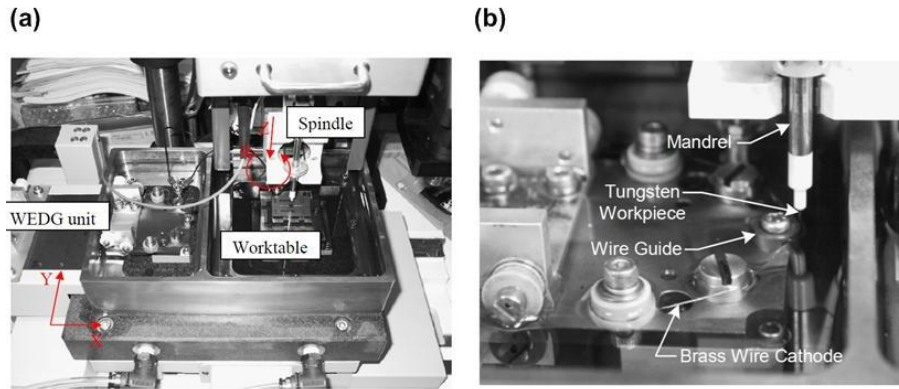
Machine MG-ED72W d'après [96]. (a) Vue générale. (b) Poste de fabrication du micro-outil par WEDG.
